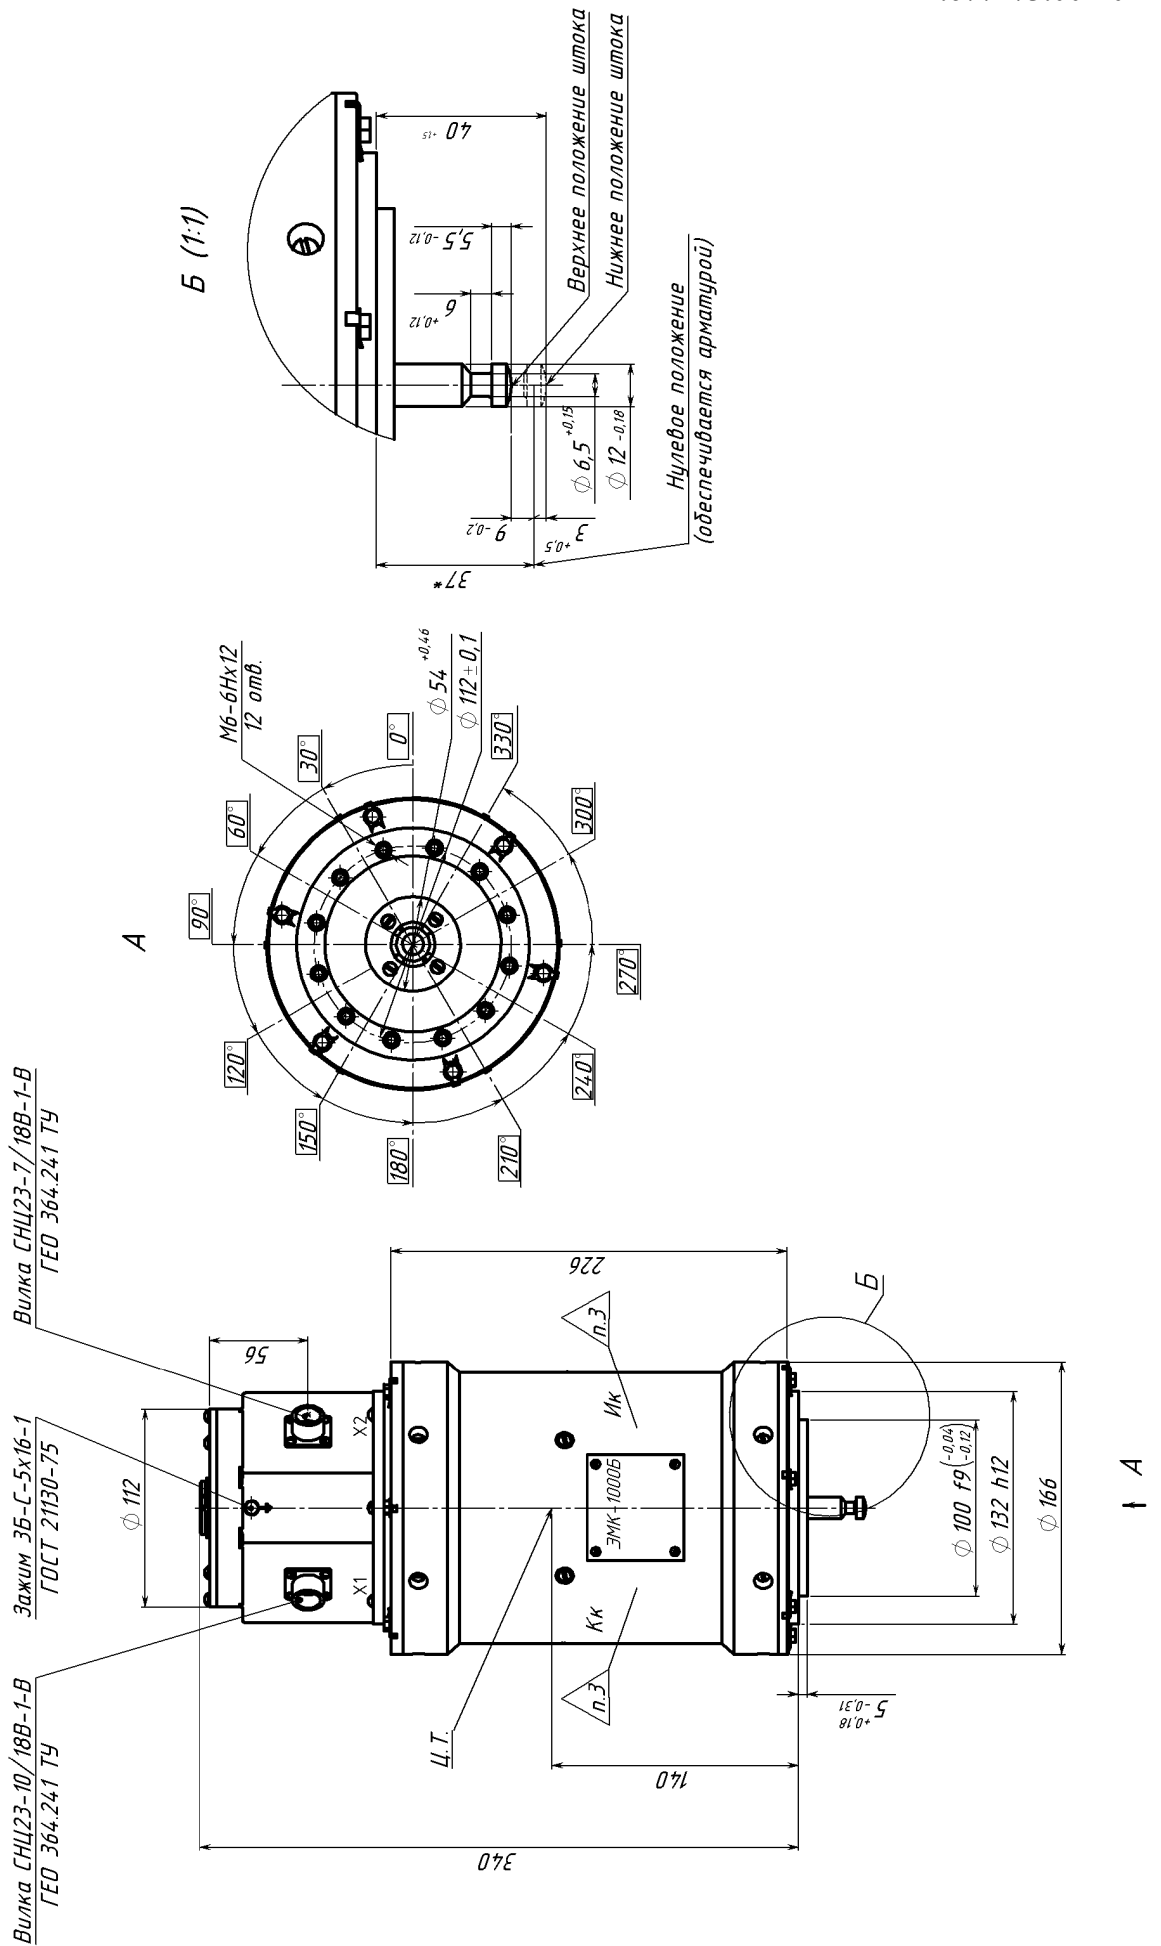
Габаритный чертеж привода ЭМК 1000Б
